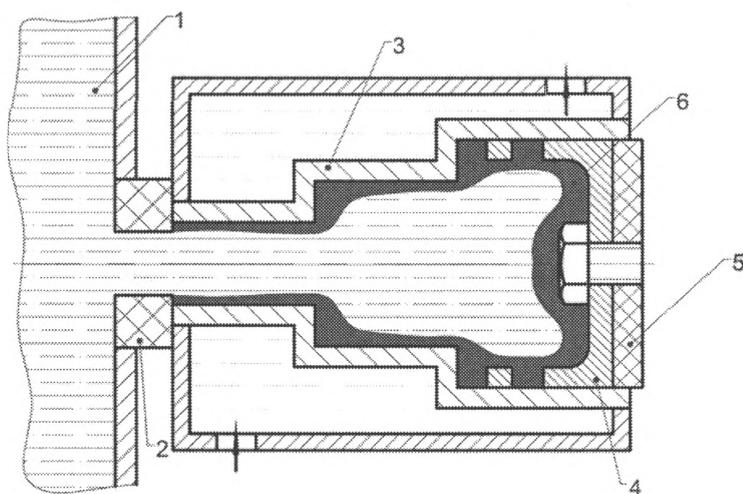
Первый цикл вытяжки «телескопической» отливки
